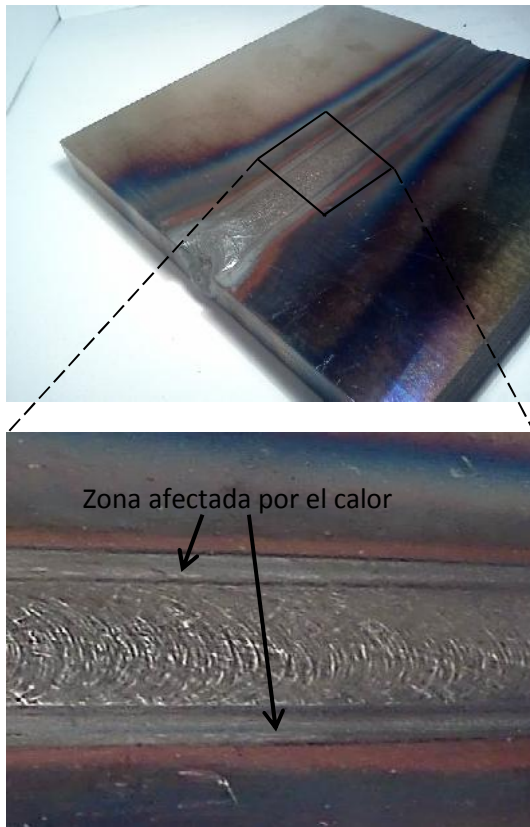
Soldadura producida por el proceso GTAW.
